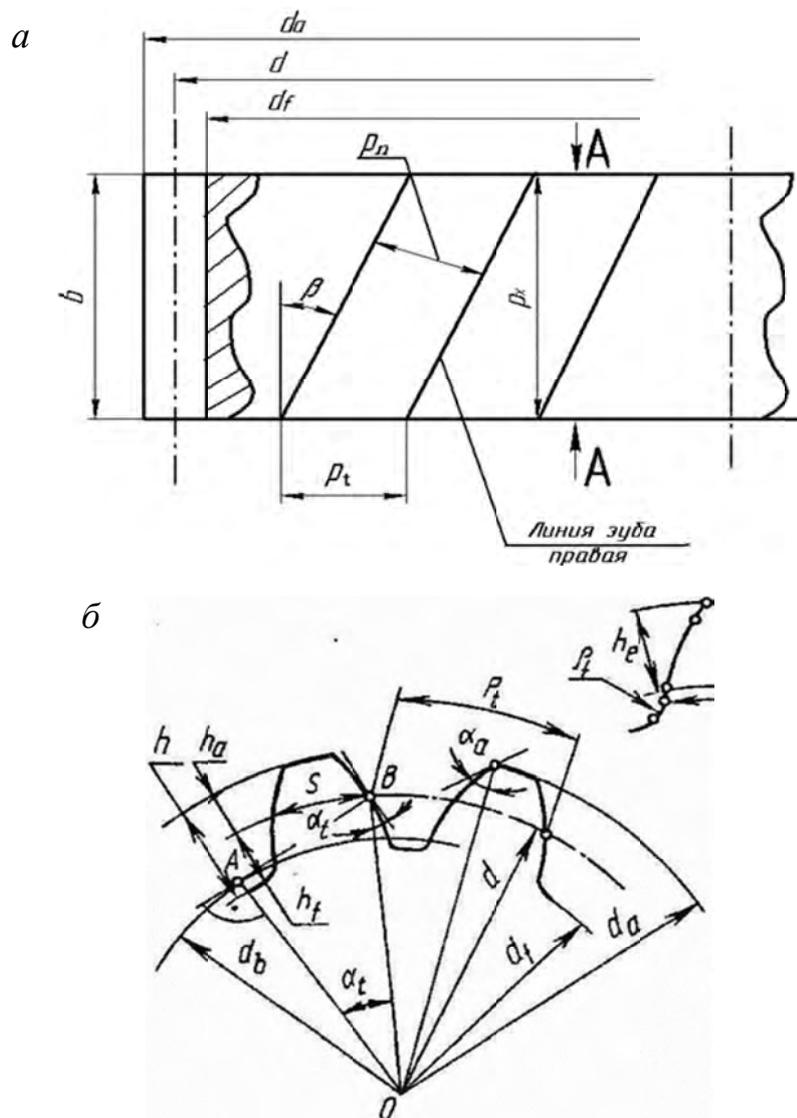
Основные геометрические параметры зубчатого цилиндрического зацепления:
